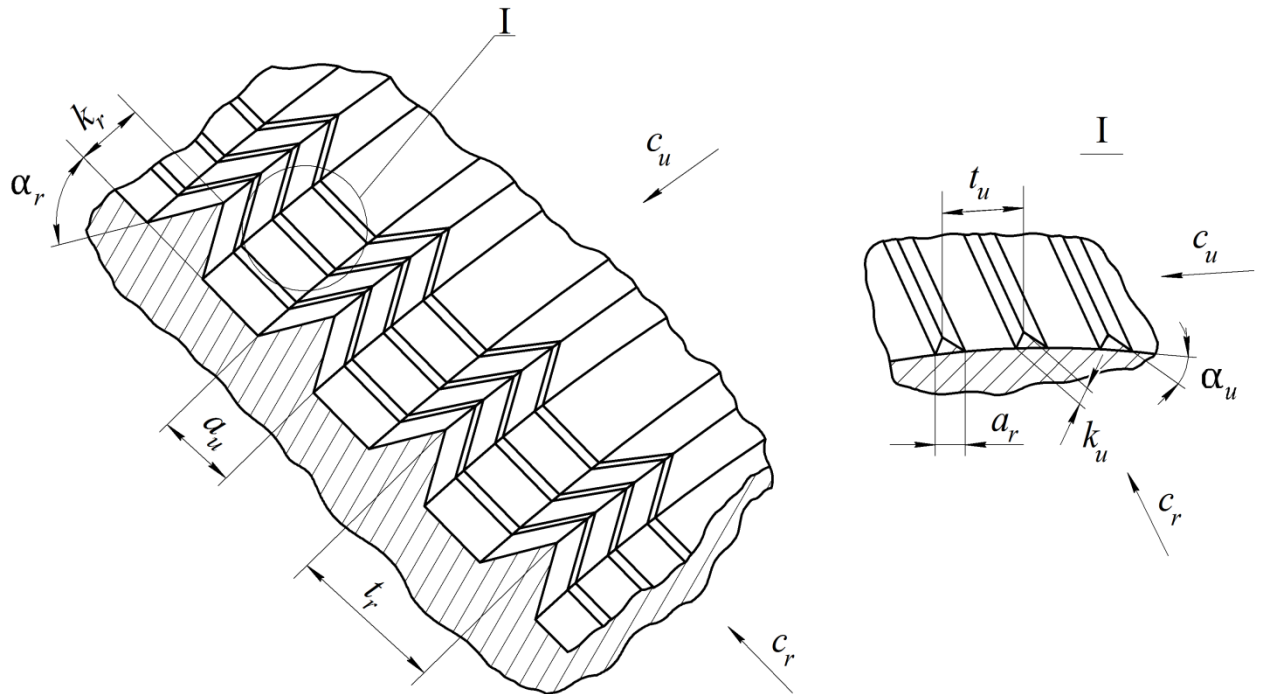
Модельная шероховатость поверхностей дисков и корпуса
